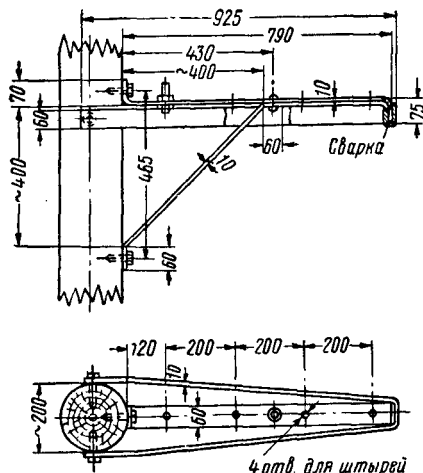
Накладка для скрещивания проводов на деревянных траверсах
